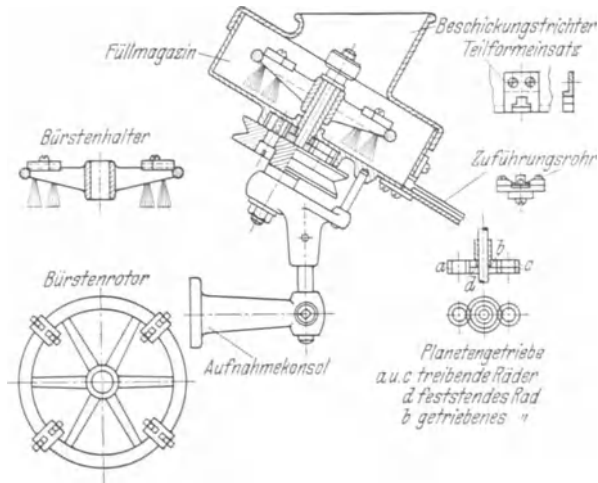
Zuführungsvorrichtung mit Bürstenrotor für Druckknöpfe.
